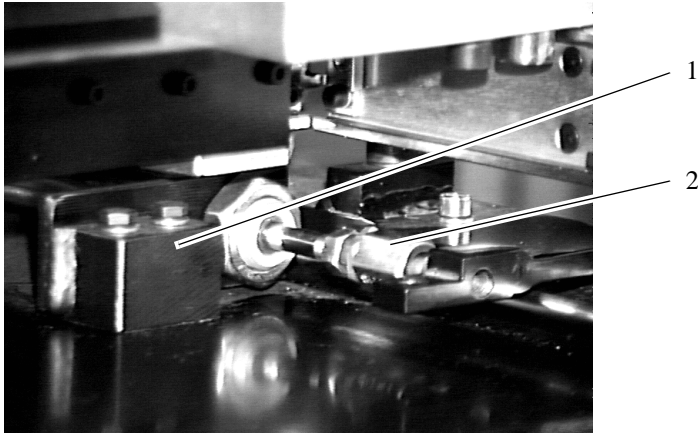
Befestigungswinkel Pneumatik-Zylinder
